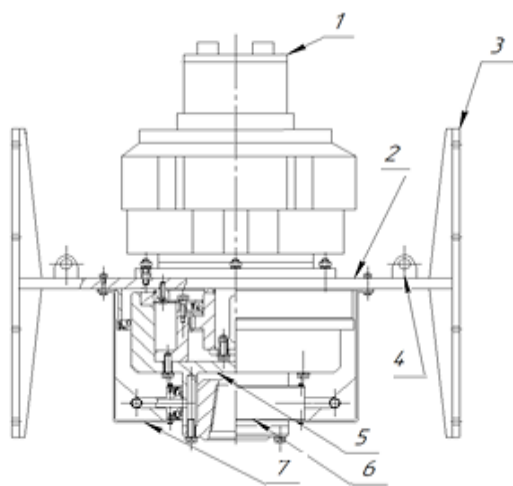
Привод вращения бурового става с высокомоментным гидромотором без редуктора:
